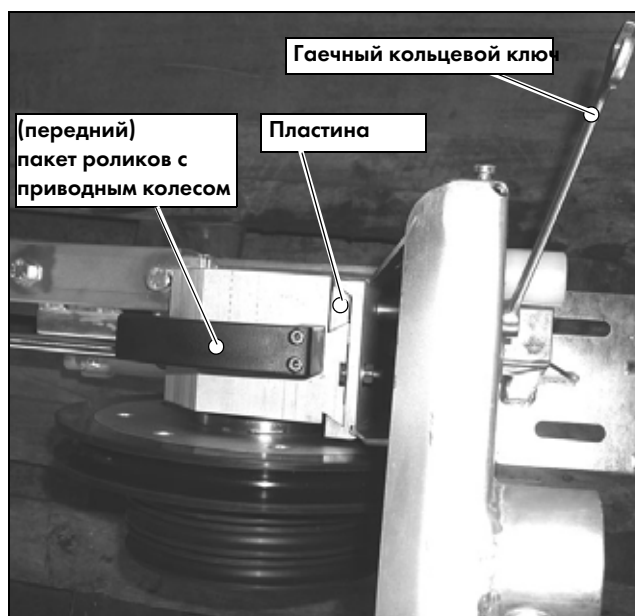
Смонтированный передний пакет роликов CSA•100 (с приводным колесом)
